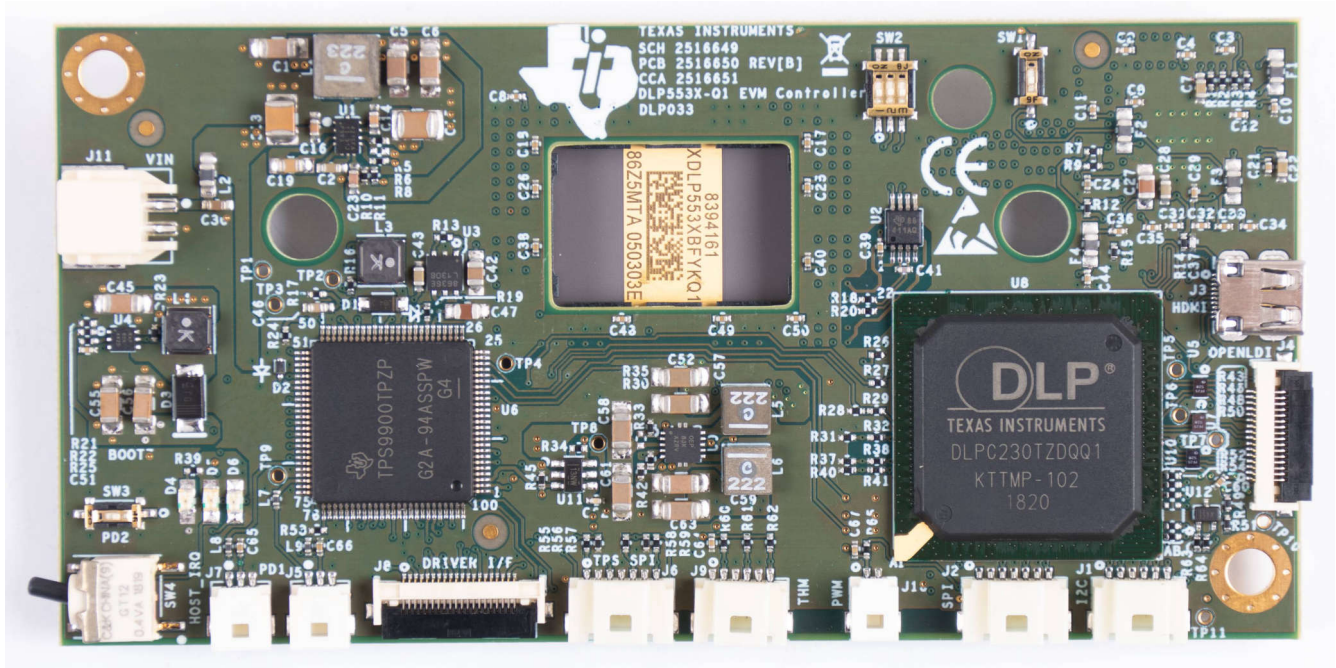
DLP5532PROJHBQ1EVM 控制器 PCB
